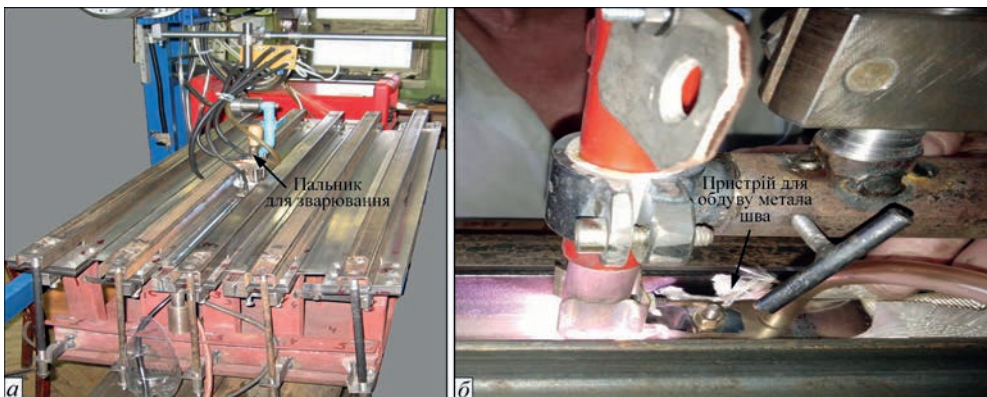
Зовнішній вигляд комплексу для зварювання ТІГ ММ: а – стенд для збирання та зварювання зразків; б – ТІГ-процес із використанням обдуву зовнішньої поверхні остигаючого металу шва (для сплаву ТА2)
